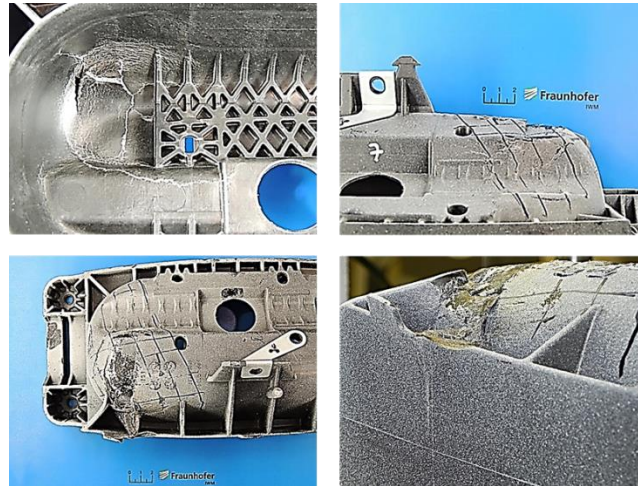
Bruchbilder Position 1 (äußere Stempelposition) bei 2 m s-1, Eindringtiefe: 18 mm (Bauteil 7)
